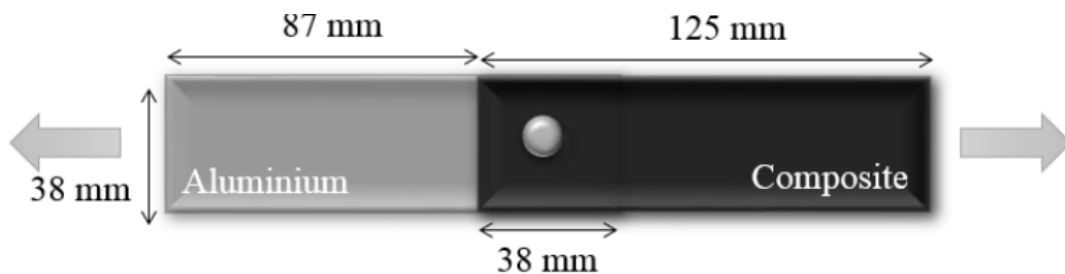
Dimensions géométriques des échantillons rivetés [3].
